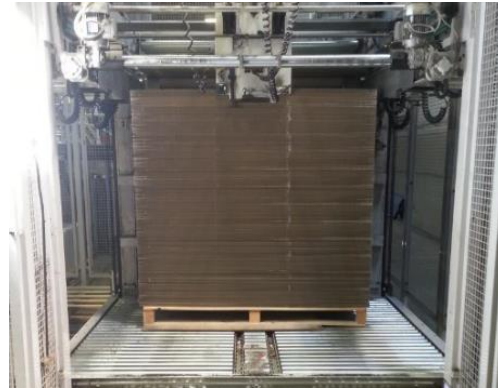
Planimetria da obra na palete (Calheiros Embalagens, 2017)
